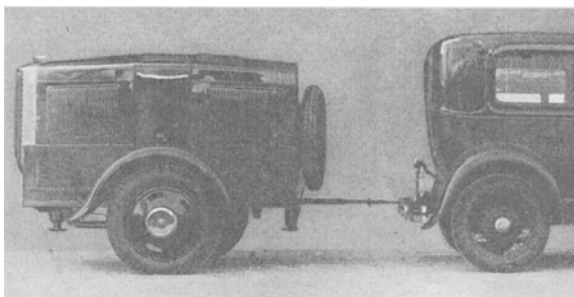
Schweißgenerator mit Benzinmotorantrieb („Schweißwagen“).
